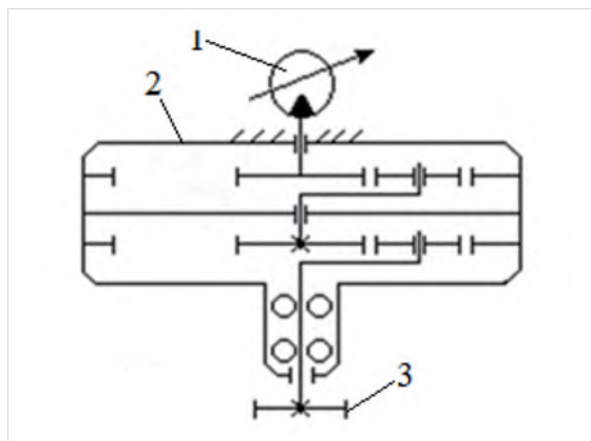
Кинематическая схема планетарного механизма поворота платформы экскаватора: 1 — гидродвигатель; 2 — планетарный редуктор; 3 — венцовая шестерня
